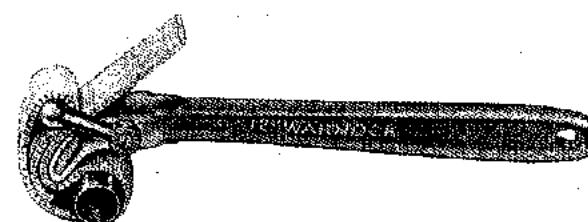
Llave de brida (Lowell Wrench Co.)
